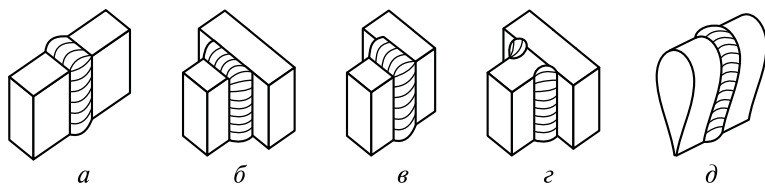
Соединения для электрошлаковой сварки:
